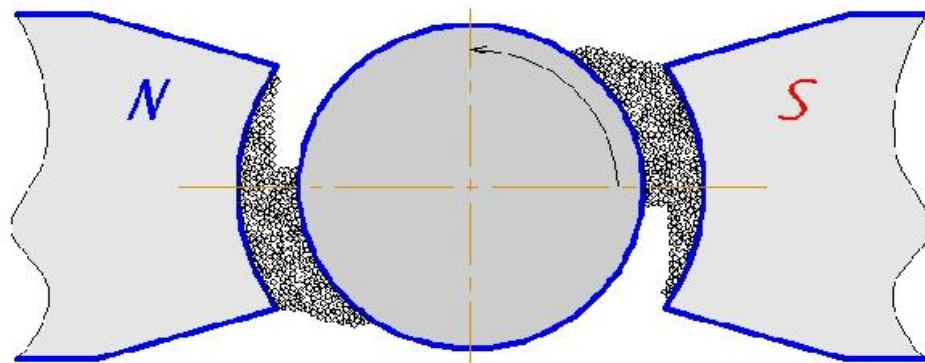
Схема станка магнитоабразивной обработки
